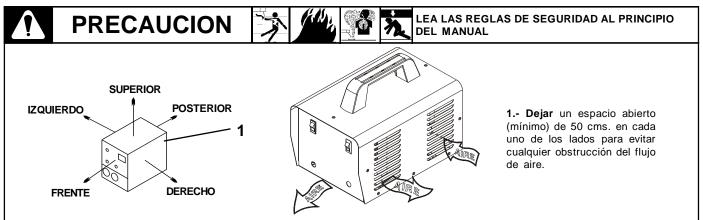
LOCALIZACION DE LA MAQUINA SOLDADORA
